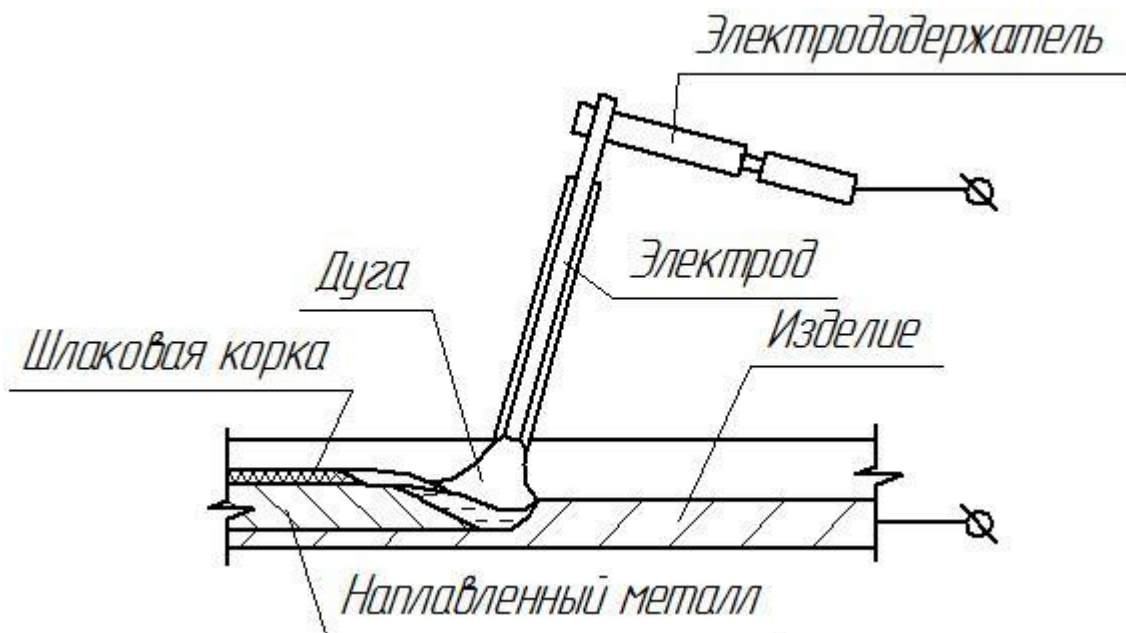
Схема осуществления дуговой наплавки штучными электродами
